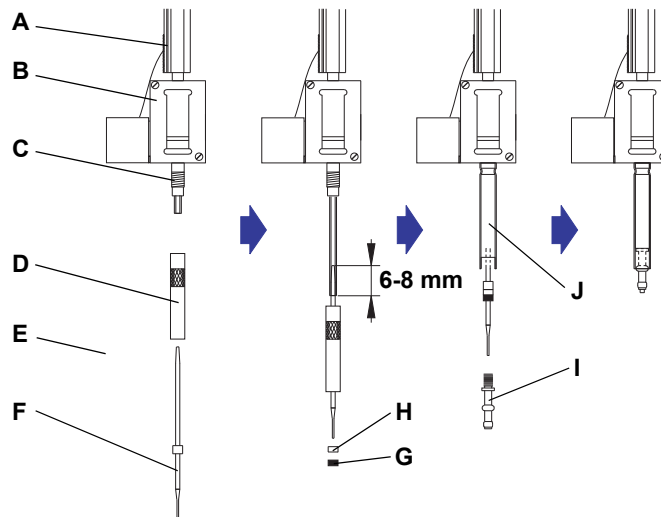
Installation du mécanisme de prélèvement des embouts jetables
